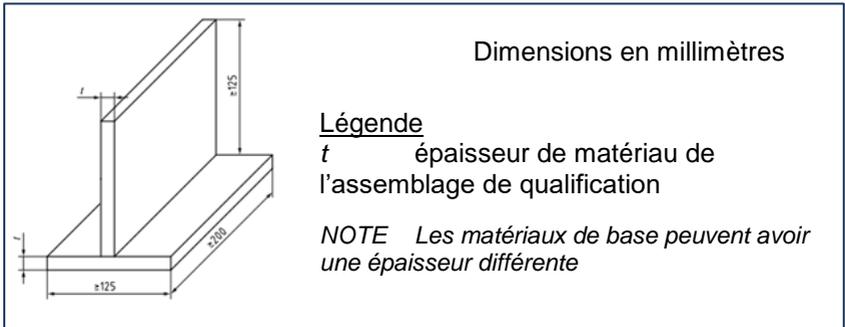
Dimensions de l'assemblage de qualification pour une soudure d'angle sur plaques
